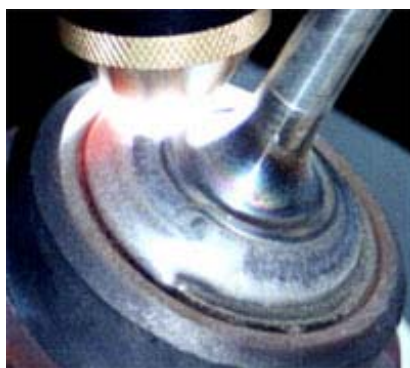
Плазменная наплавка изношенной поверхности тарелки клапана
